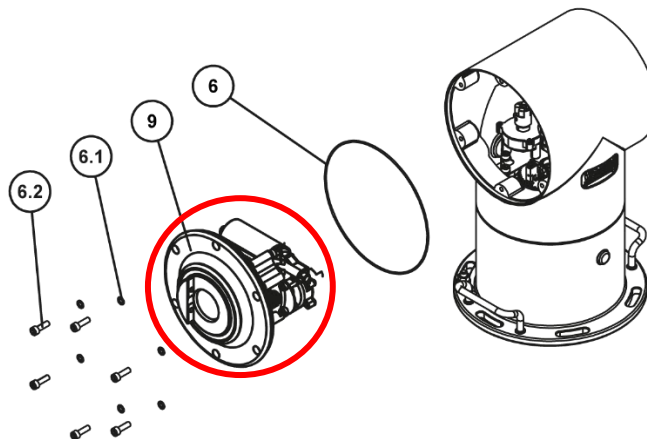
Schwenk-Neigeeinheit mit Active flange tilt und Sealing for flange
